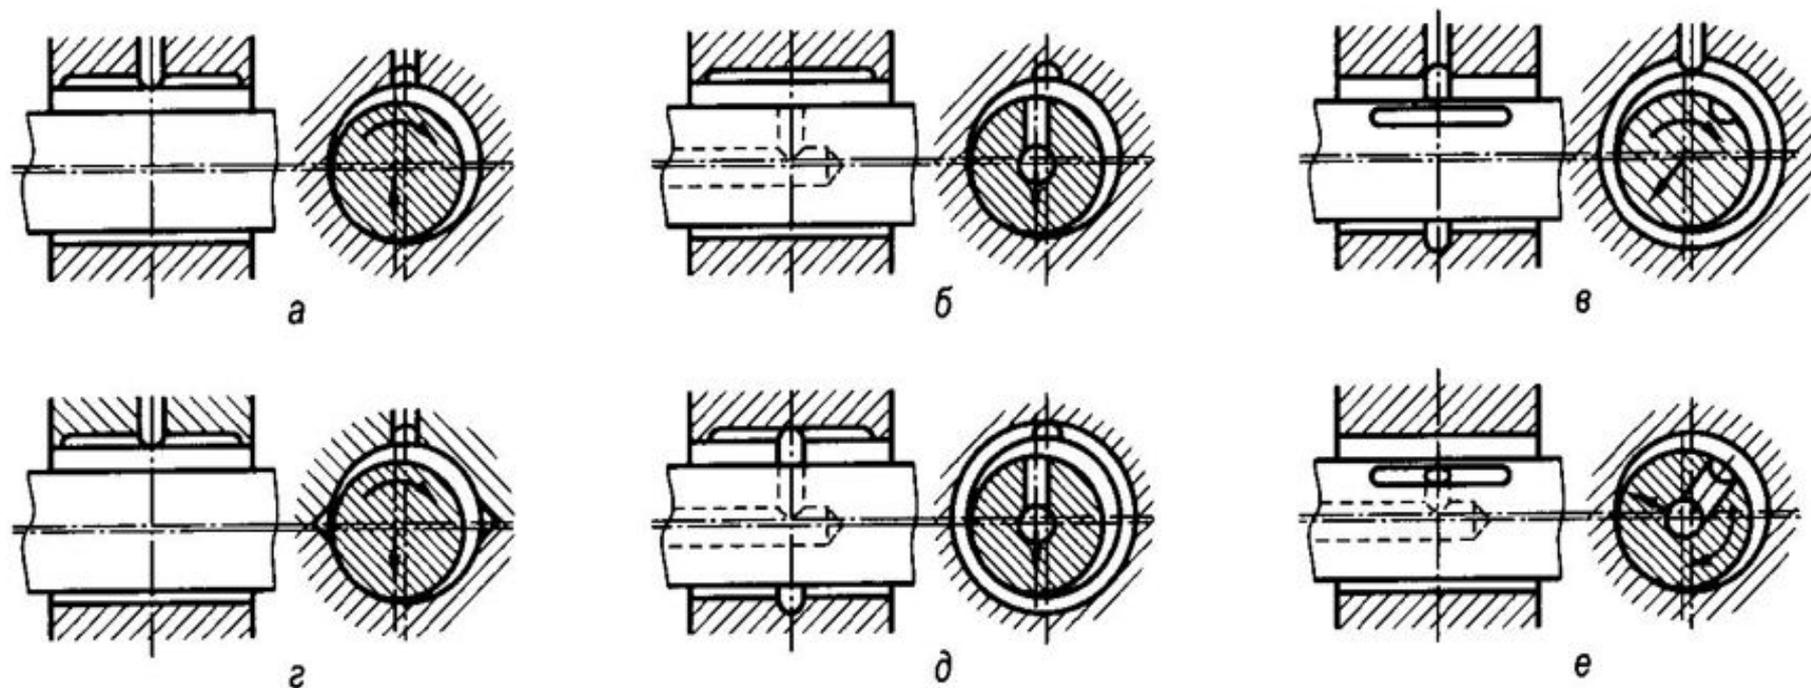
Способы подачи СМ в горизонтальный подшипник через неразъемный корпус и втулку (а, в), через вал (б, д, е) и через разъемный корпус и вкладыш (г):
